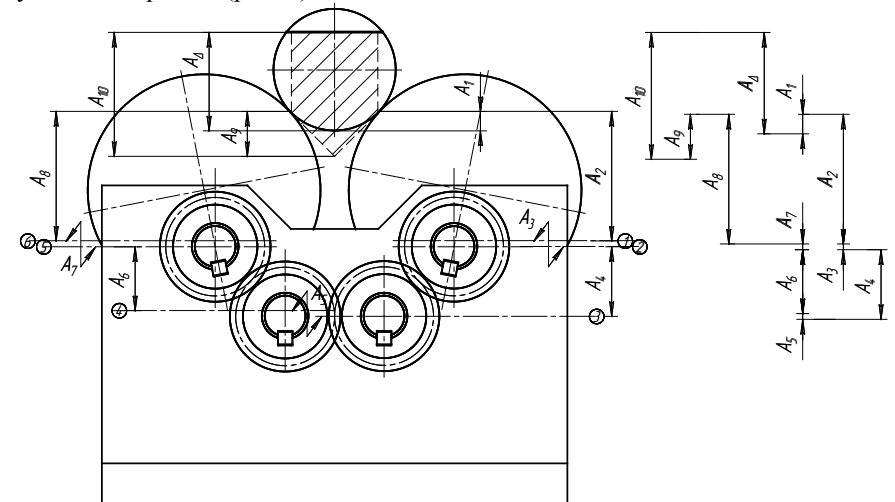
Базирующая призма (патент Украины № 31416) і розмірний ланцюг для визначення похибки базування при фрезеруванні лиски, паралельної до стола верстата
